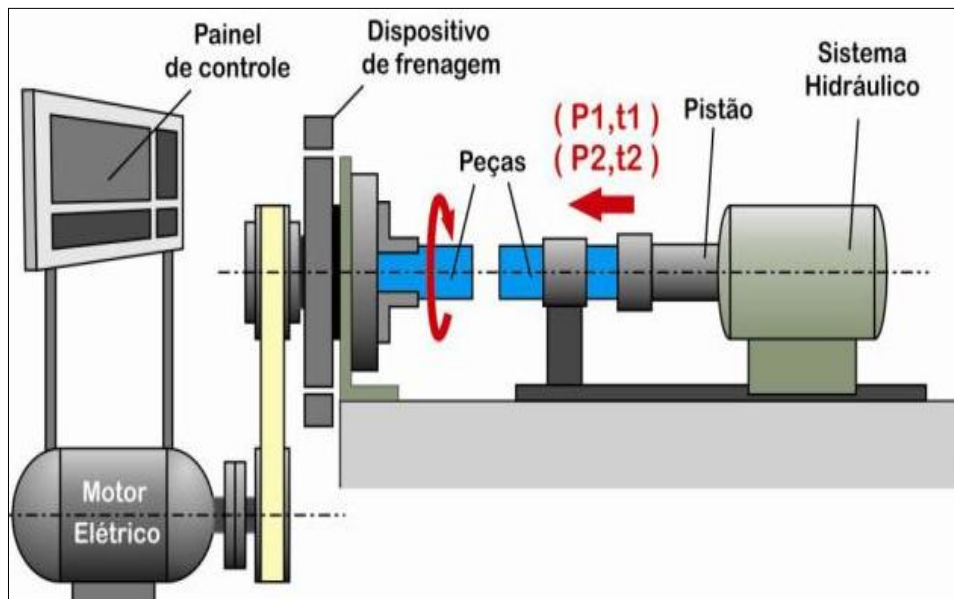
Equipamento de soldagem por fricção de arraste contínuo.
